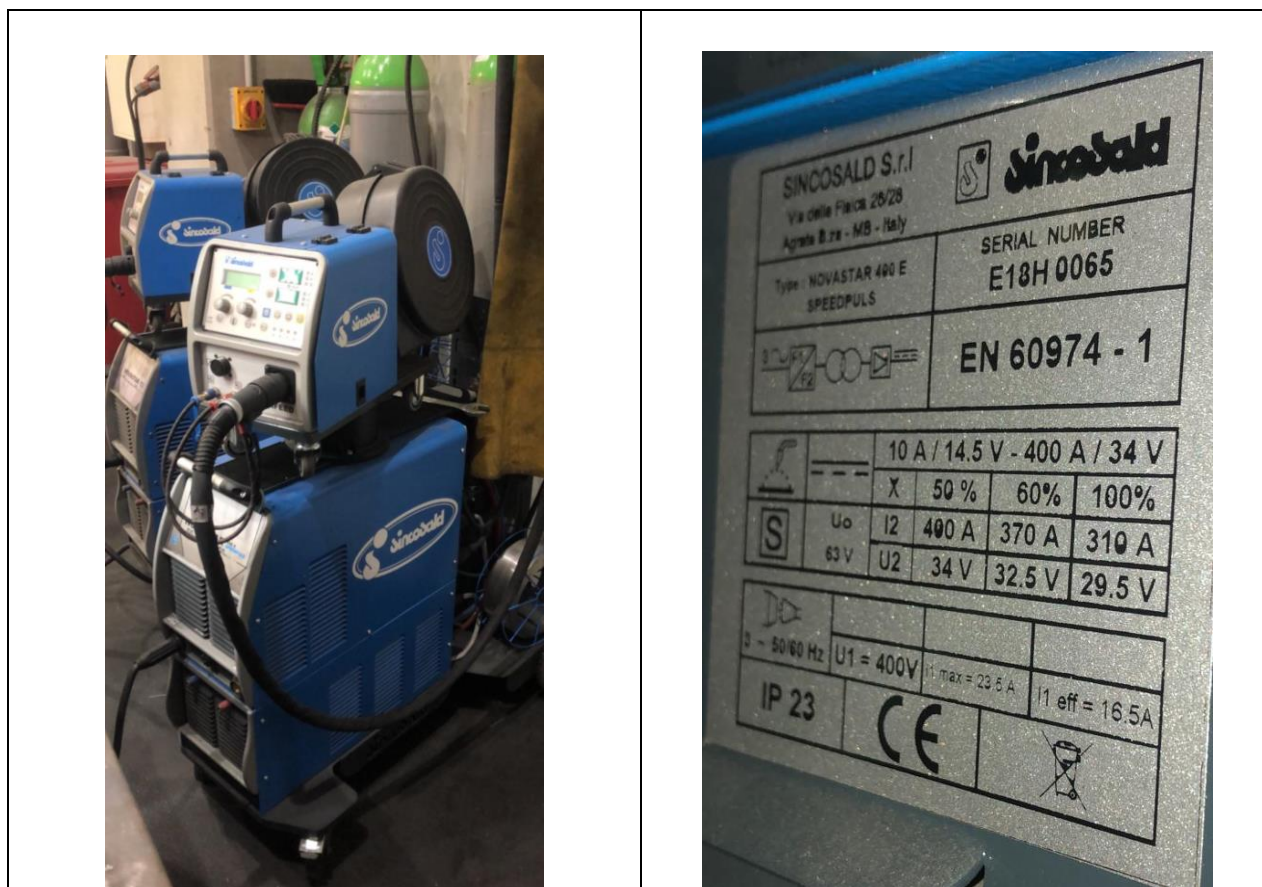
Máquina soldadura MAG empleada en las pruebas y placa de características. Fuente: Propia.
